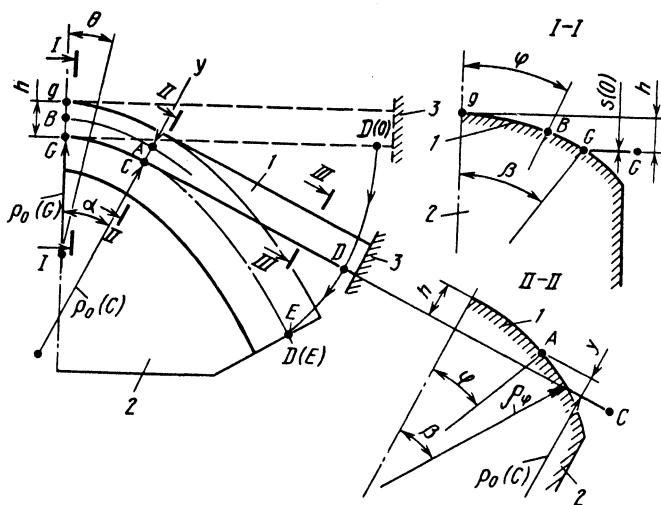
Обтяжка заготовки с цилиндрическим gG и плоским GG участками по поверхности пуансона, имеющей двойную кривизну: 1 - заготовка; 2 - пуансон; 3 - захват
